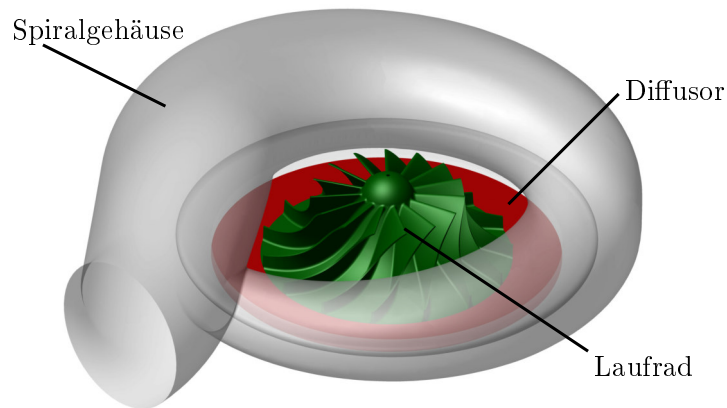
Gesamtansicht des untersuchten Radialverdichters mit Spiralgehäuse
